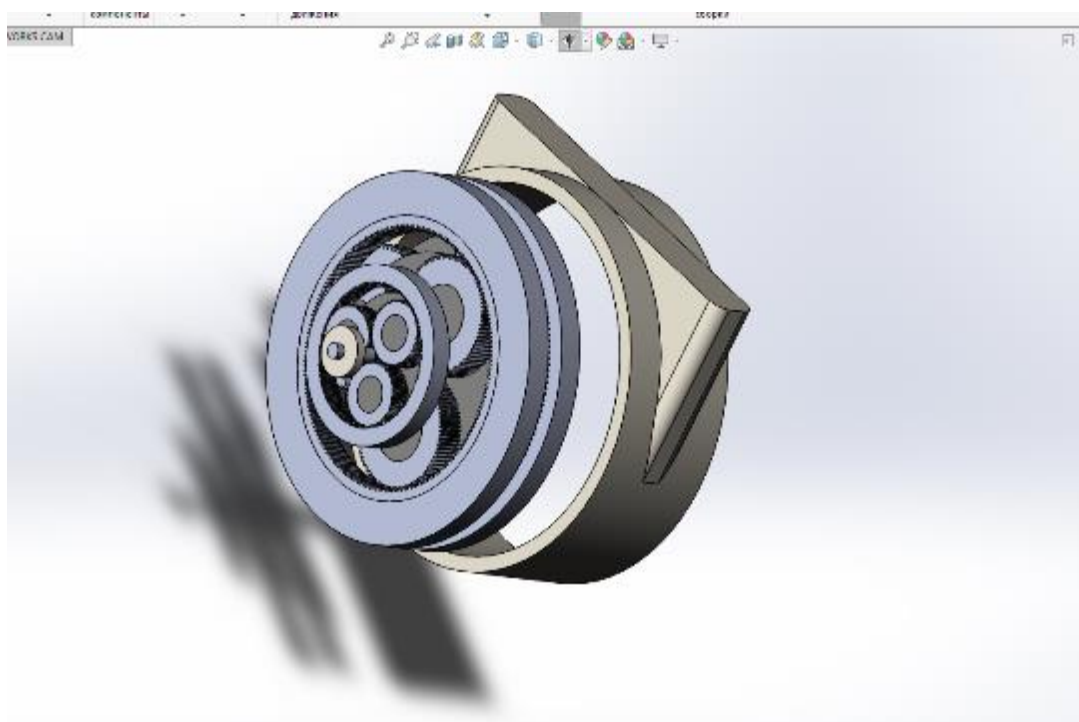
Корпус редуктора и посадочное колесо 2 ступени
